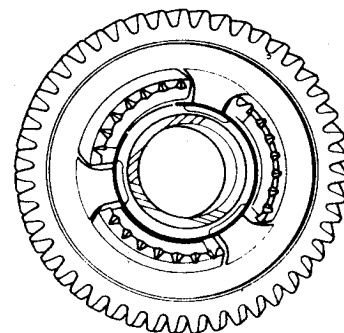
Colocación del resorte del sincronizador en el engranaje libre de 1ª.
